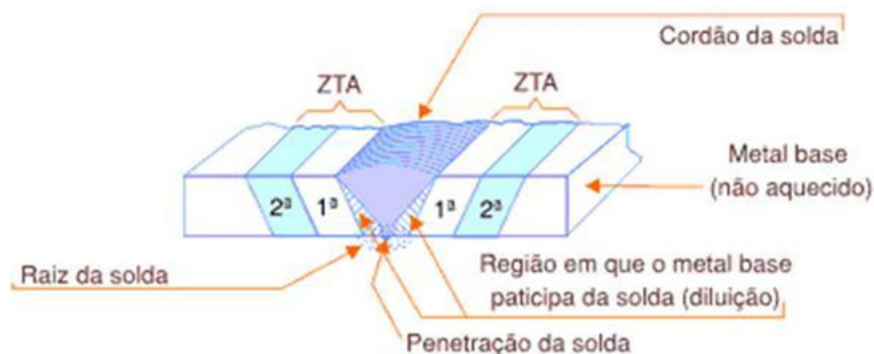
Nomenclatura de soldagem por fusão <sup>(4)</sup>.
